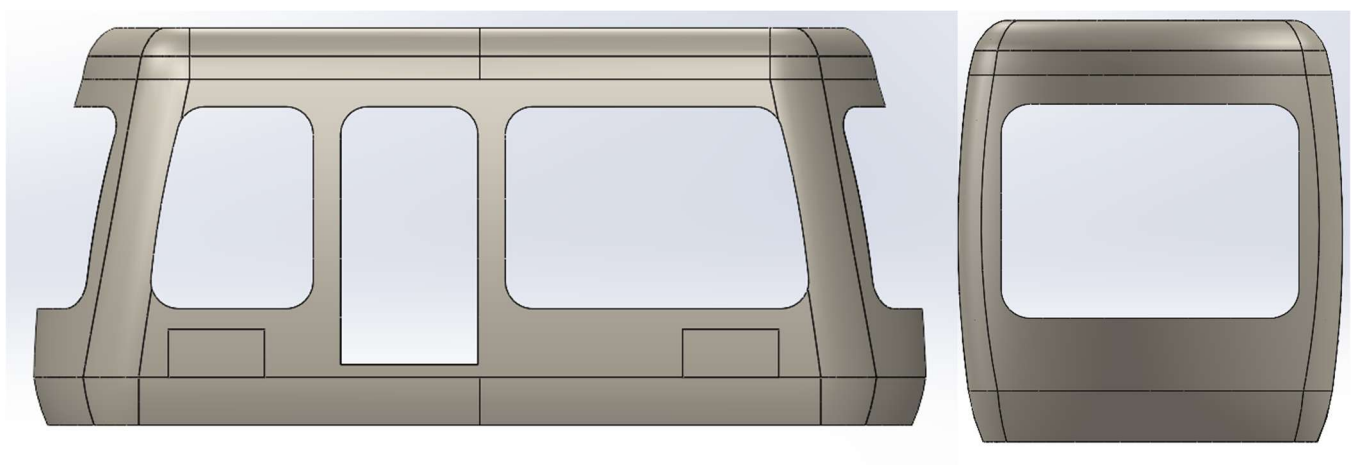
Alzado y vista lateral del diseño final de la estructura con los faldones y acabados.
